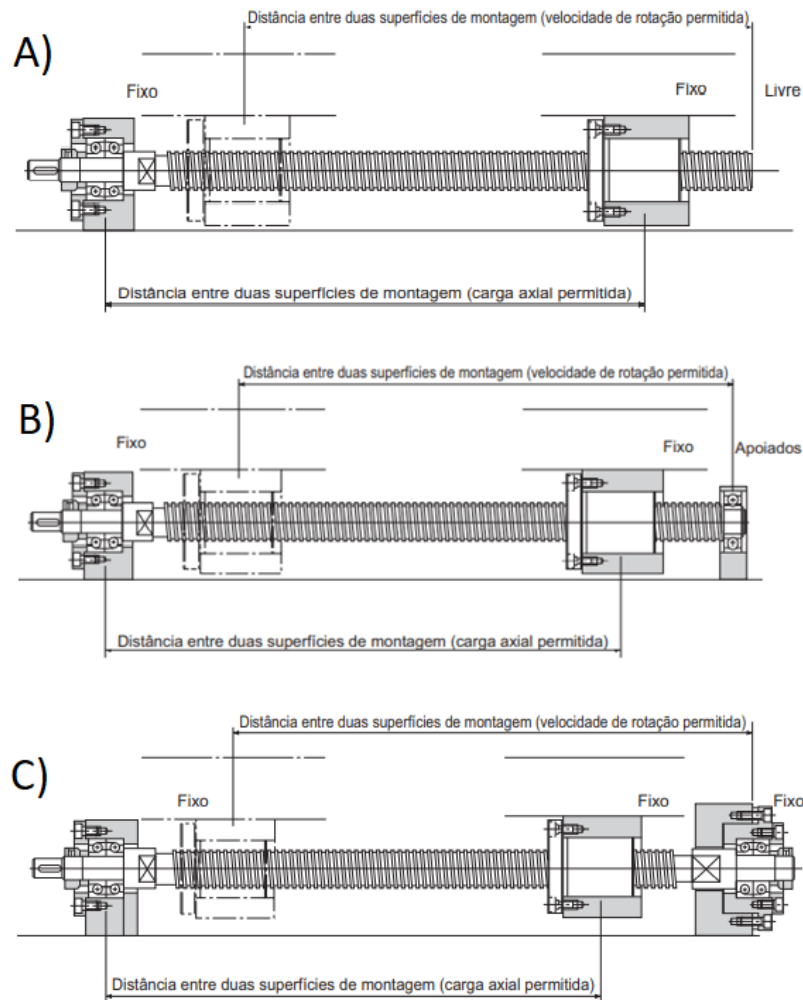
Opções de montagem para o parafuso de esferas: A) Fixo-livre; B) Fixo-apoiado; C) Fixo-Fixo- [25]
